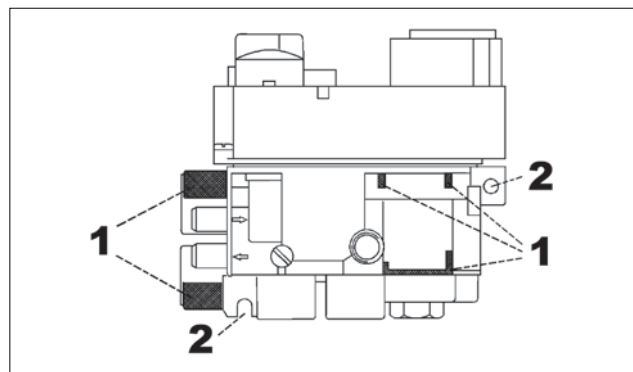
1 = Zones de serrage, 2 = Points de montage
